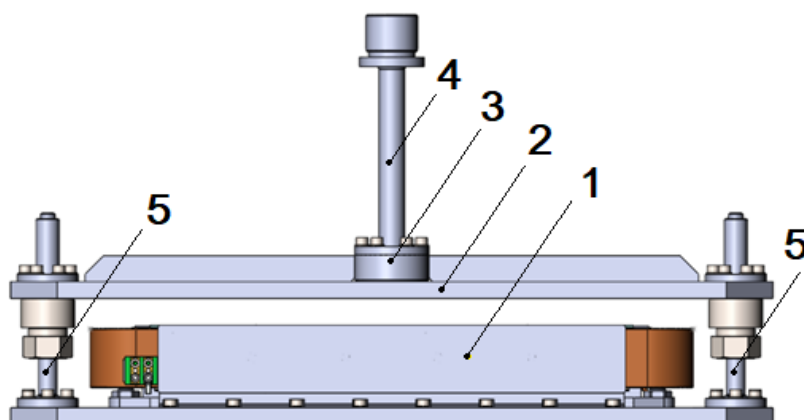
Приспособление с закрепленным на нем магнитом (1) и стальная пластина (2), соединенная с помощью узла крепления (3) с динамометрической штангой (4) испытательной машины 1958У-10-1; направляющие штыри (5) приспособления служат для обеспечения лучшей параллельности относительного перемещения магнита и пластины
